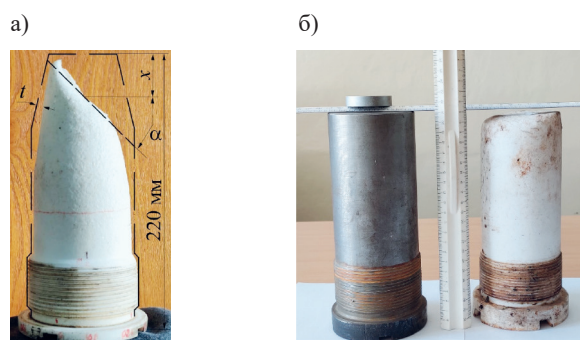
Вид изношенных форсунок из фторопласта с конической носовой частью (а) и цилиндрической формой (б)
